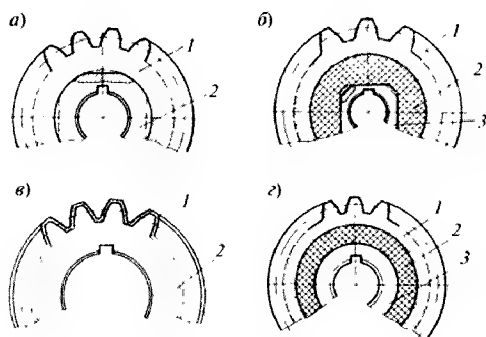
Шлифовальный шевер с наружным расположением зубьев:
